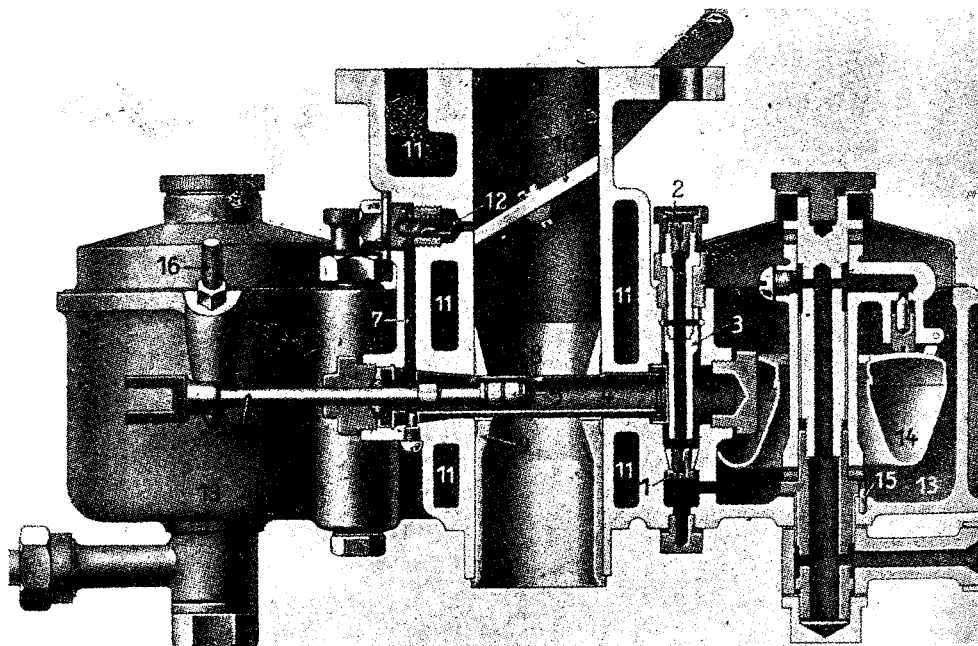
SECȚIUNE PRIN CARBURATORUL DUBLU GRAETZIN. — 1 Jicler principal; 2 Jicler pentru adaus de aer; 3 Suport de jiclere; 4 Teavă transversală. 5 P'ston pentru schimbare de combustibil; 6 Tijă de piston; 7 Canal pentru mersul în gol; 8 Orificiu de esire a combustibilului; 9 Pulverizator; 10 Clapet de strangulare; 11 Canale de încălzit; 12 Jicler pentru mersul în gol; 13 Camera de flotor; 14 Flotor; 15 Cui de fixare al suportului flotorului; 16 Dispozitiv de apăsare asupra flotorului.
